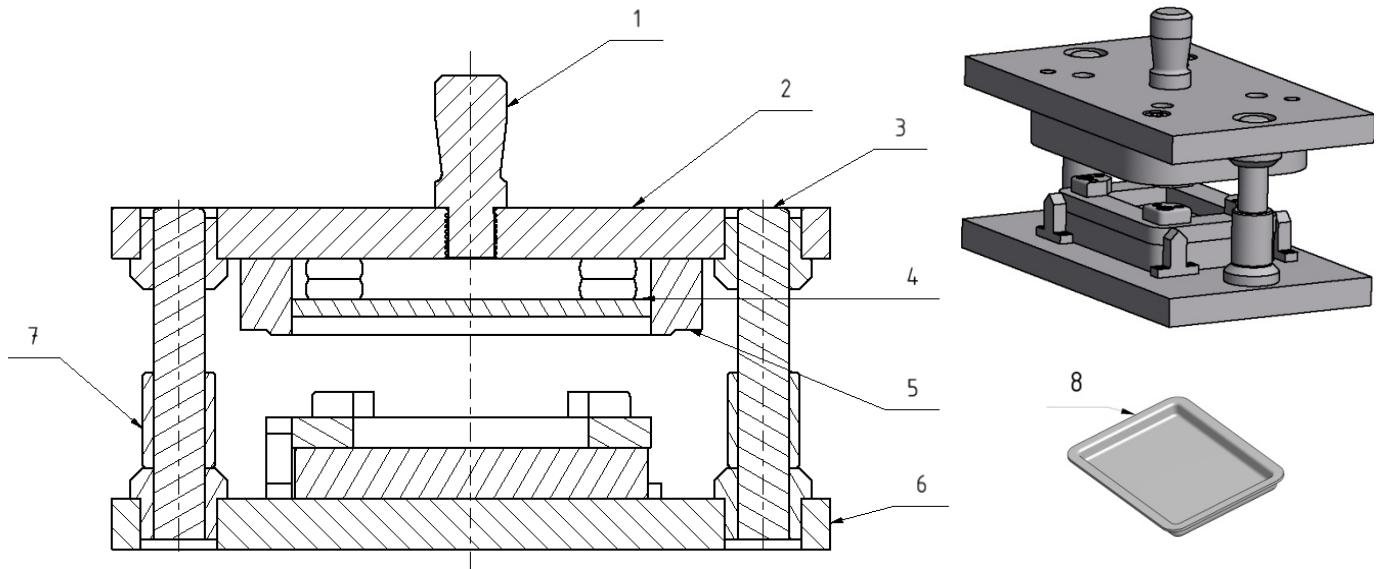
Beschneidewerkzeug für Tiefziehform
